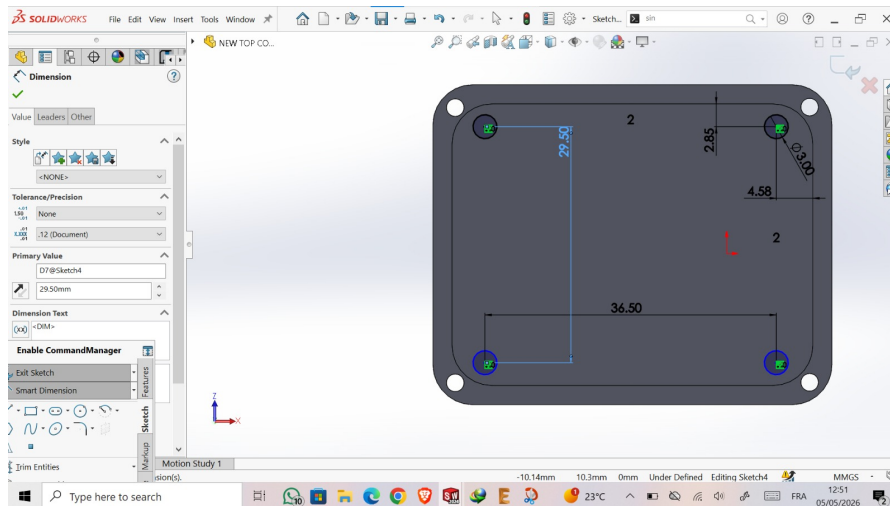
Dimensions du support interne prévu pour le PCB.
